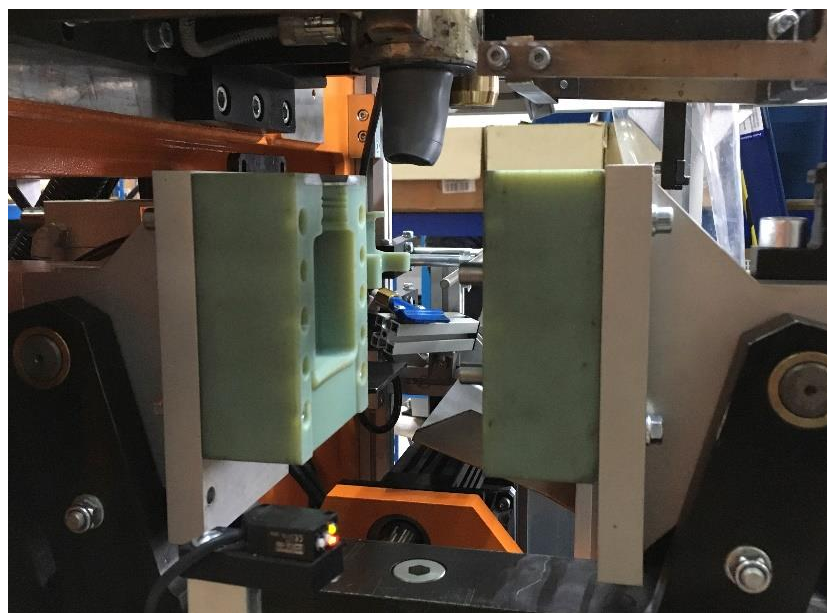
Obrobena tělo formy vyrobené 3D tiskem PolyJet
